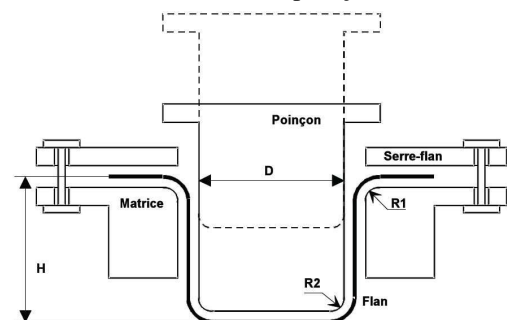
Géométrie du flan et de l'outil d'emboutissage
